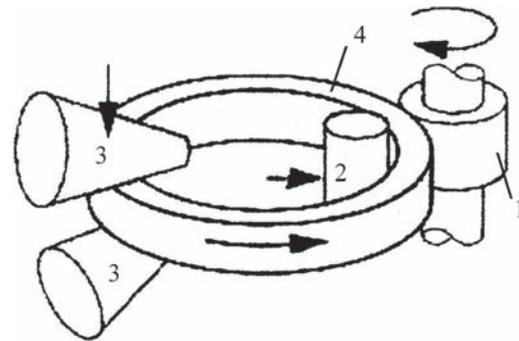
Схема горячей кольцераскатки: 1 — главный валок; 2 — дорновой валок; 3 — осевые валки; 4 — кольцо
